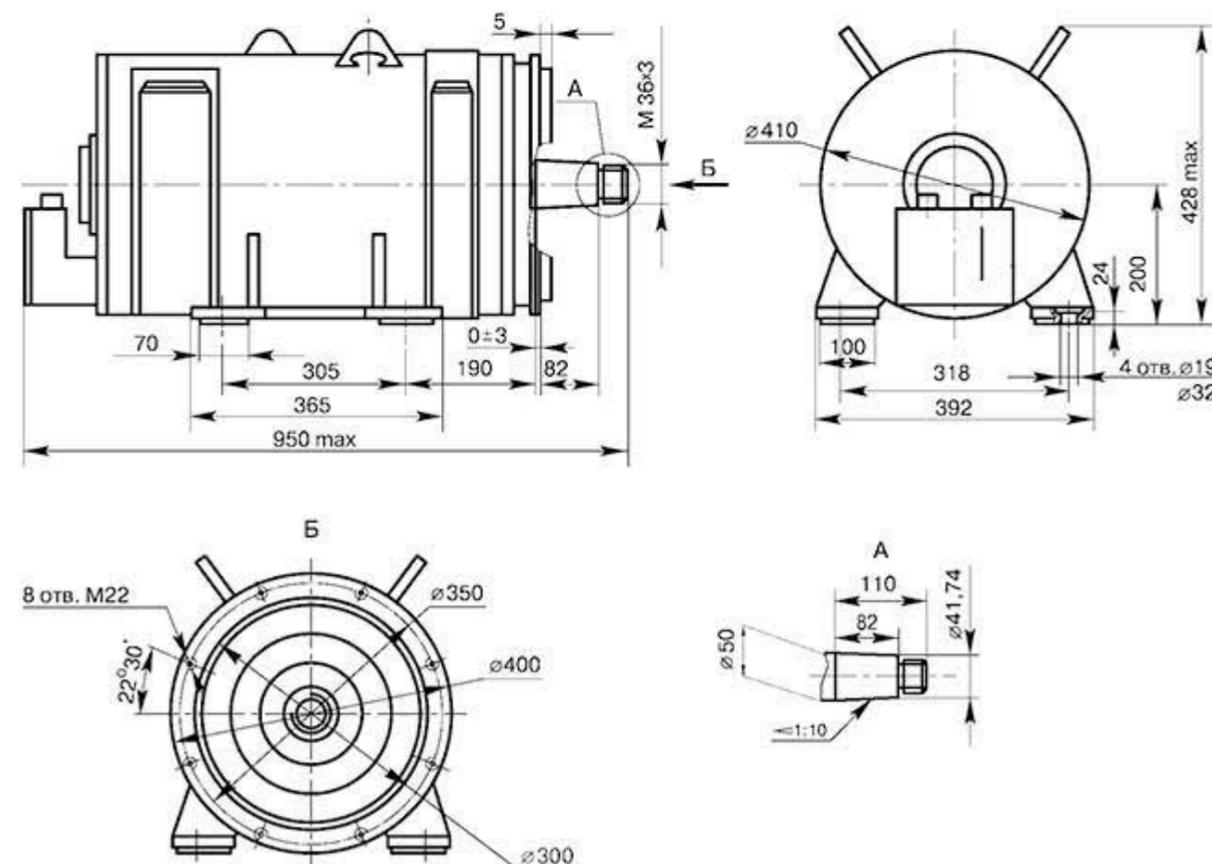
Габаритно-установочные размеры электродвигателей 4ПНЖ200М
